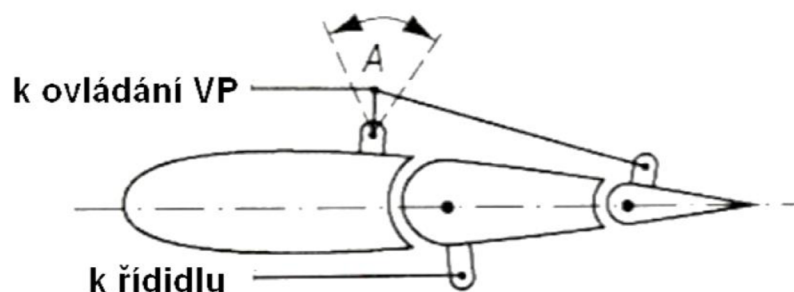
Příklad konstrukčního provedení vyvažovací plošky [2]
